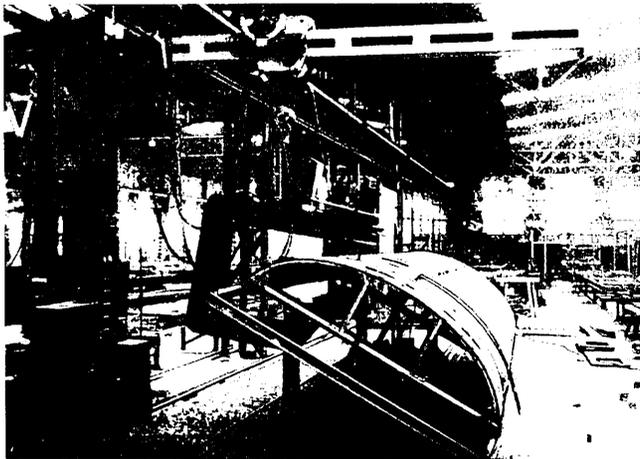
Punktschweißmaschine mit großer Ausladung der Fa. Beuchelt u. Co., Grünberg (Schlesien).
